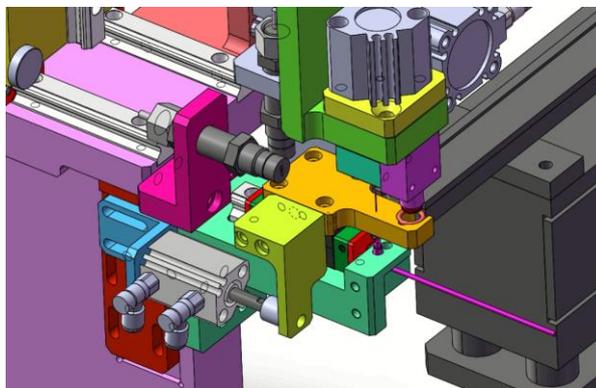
Máquina de separación de junta tórica 2. Fuente:propia
